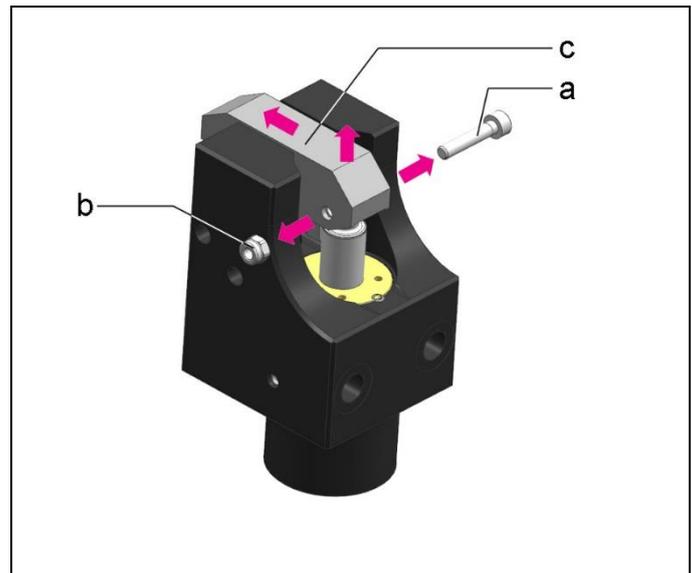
Brides de serrage avec palonnier, démontage du levier de serrage
